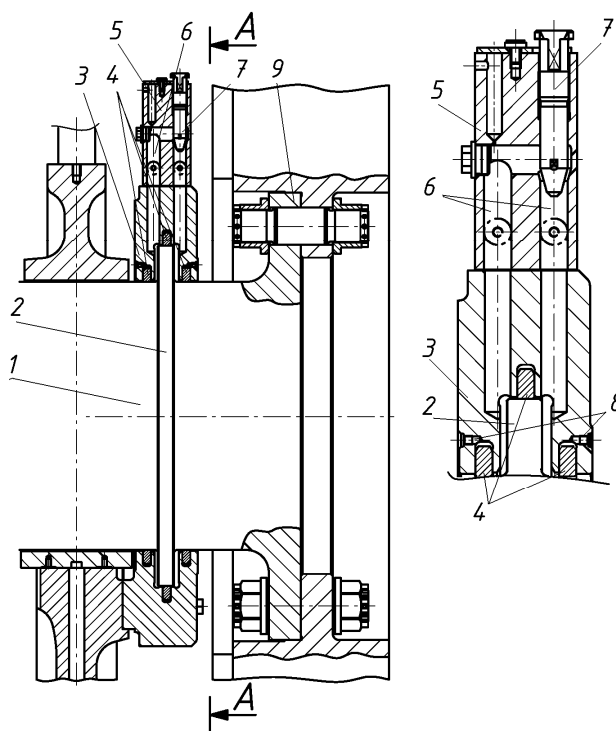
Демпфер осьових коливань колінчатого вала: 1 – шийка колінчатого вала двигуна; 2 – кільцевий виступ; 3 – гідравлічна камера; 4 – ущільнення гідравлічних порожнин; 5 – дросельний пристрій; 6 – П-образний канал; 7 – конічний запірний пристрій; 8 – дренажні отвори для зливу масла; 9 – фланець кріплення демпфера крутильних коливань
